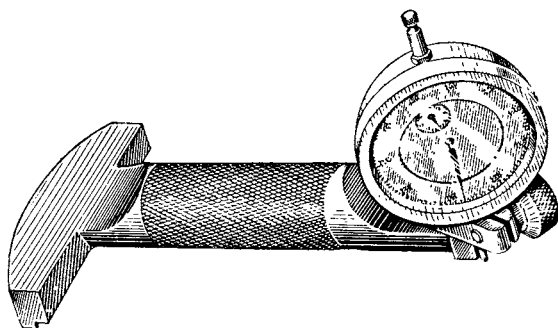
Приспособление В-49079-П-36 для проверки превышения гильзы над плоскостью рубашки цилиндров двигателя
